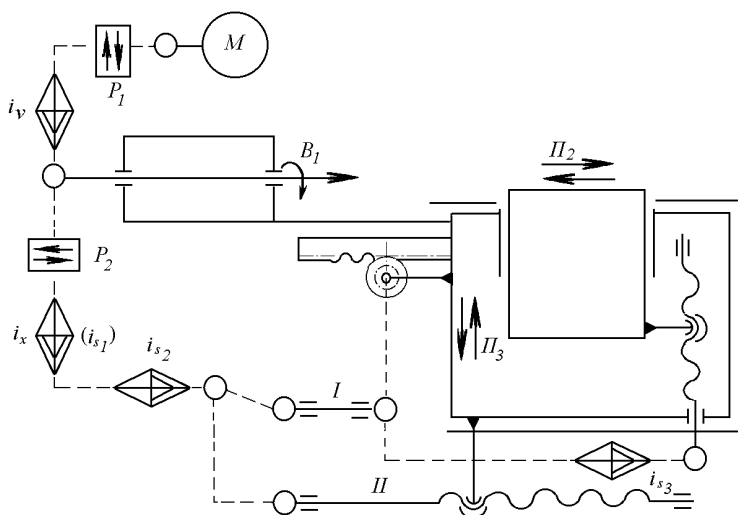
Структурная кинематическая схема токарно-винторезного станка
